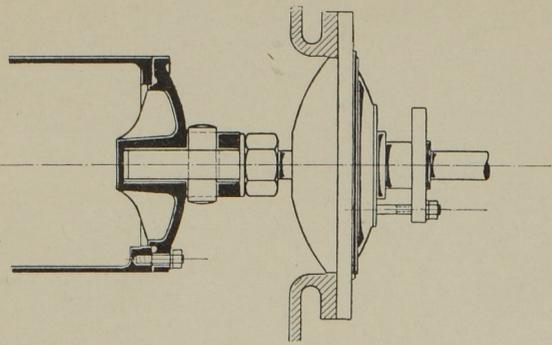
Befestigung der Kolbenstange mit dem Pumpenkolben. Masst. 1:15.
